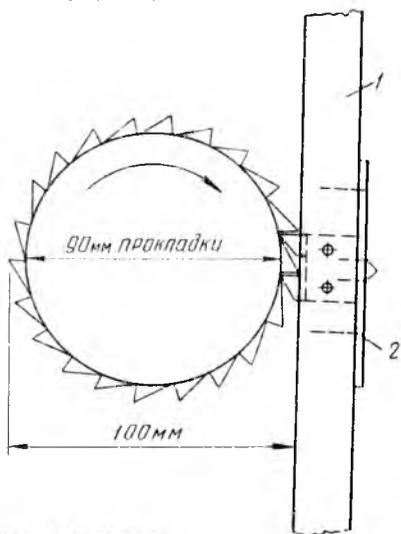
Гребенка: 1 — корпус; 2 — крепление гребенки к корпусу
